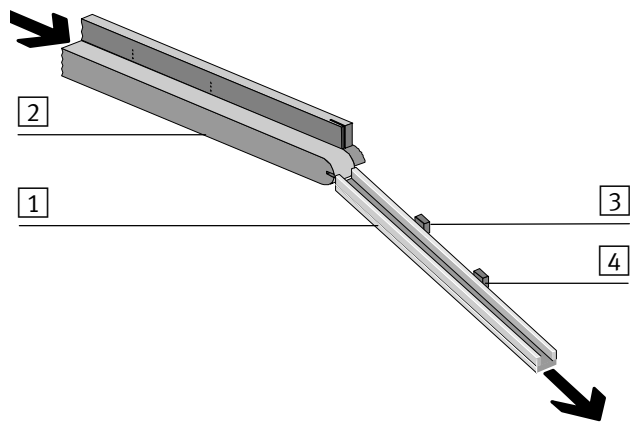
/7: Staustrecken-Kontrolle mit Schaltverzögerung
